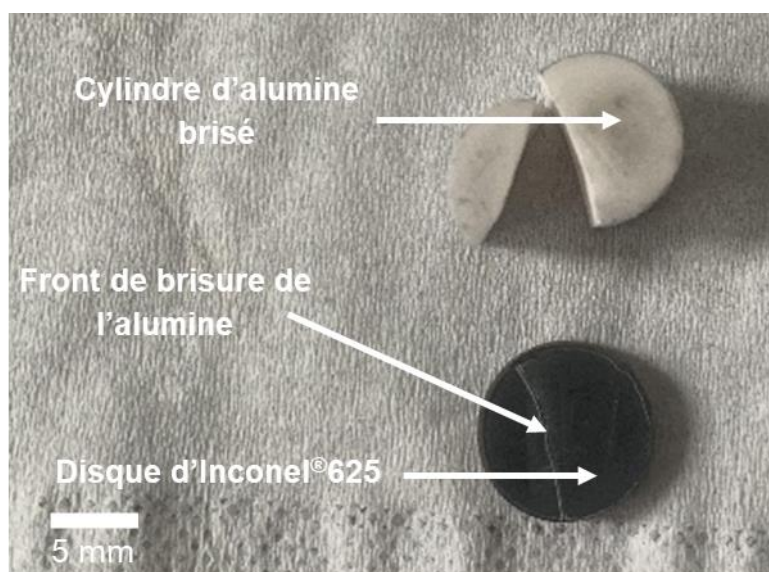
Essai d'assemblage Inconel®625 / alumine par thermocompression à 900 °C pendant 3 h de disques de 8 mm d'épaisseur.
